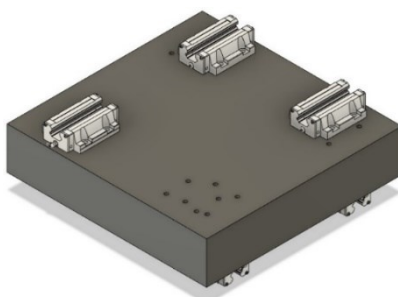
Conjunto montado de insertos (parafusos), nivelador da guia e guia.
